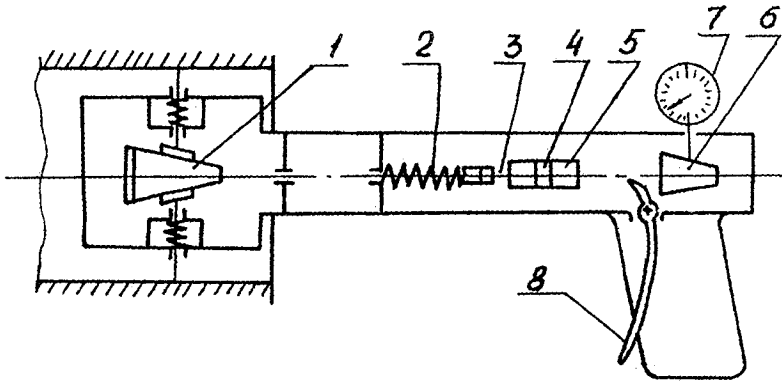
Вимірювальний механічний пристрій з індикатором
